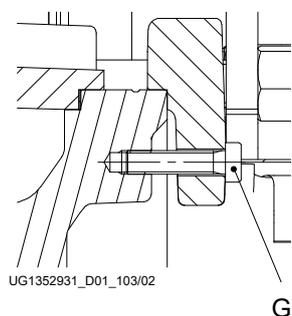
Punti di serraggio viti, versione con coperchio del corpo agganciato:
